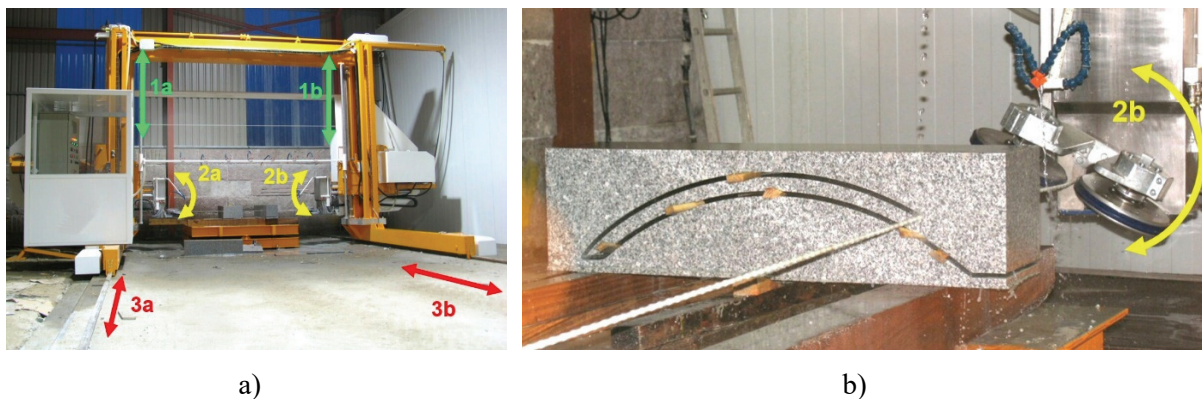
Máquina de corte de pedra com fio diamantado
